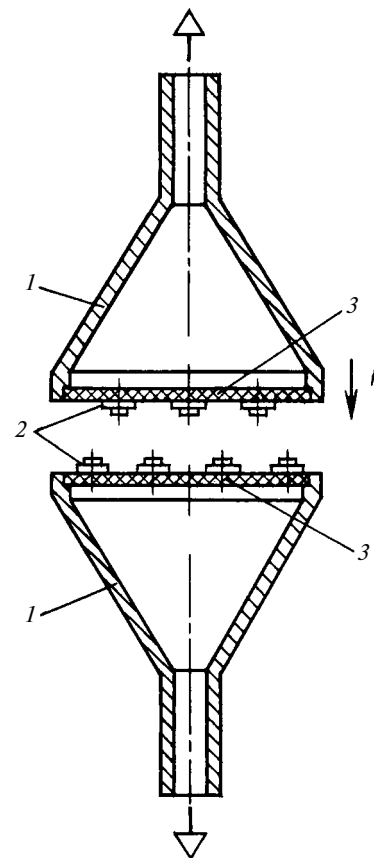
Схема групповой сортировки деталей с помощью вакуумных захватов с пористыми вставками
